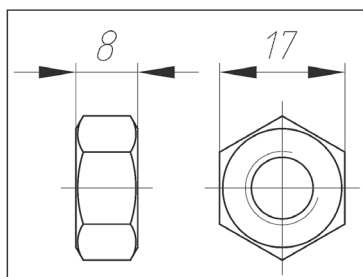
Размеры детали «Гайка шестигранная ГОСТ 5915–70» из Базы элементов
